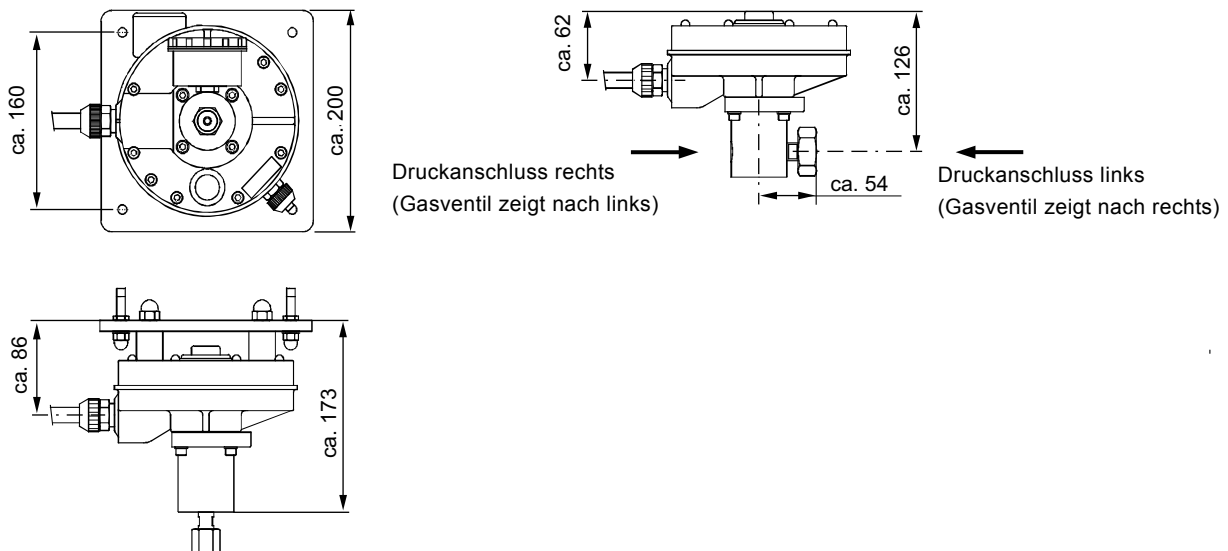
Maßzeichnung Vakuumregler an Montageplatte
